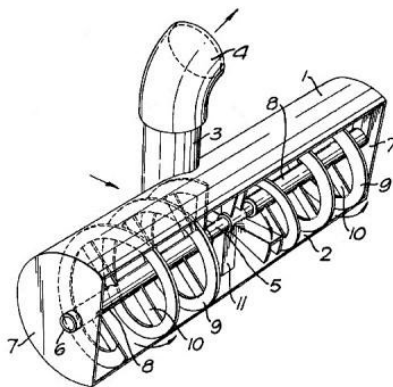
Фрезерный питатель с интенсификатором в виде лопаток коробчатой формы (патент Норвегии № 138666)
